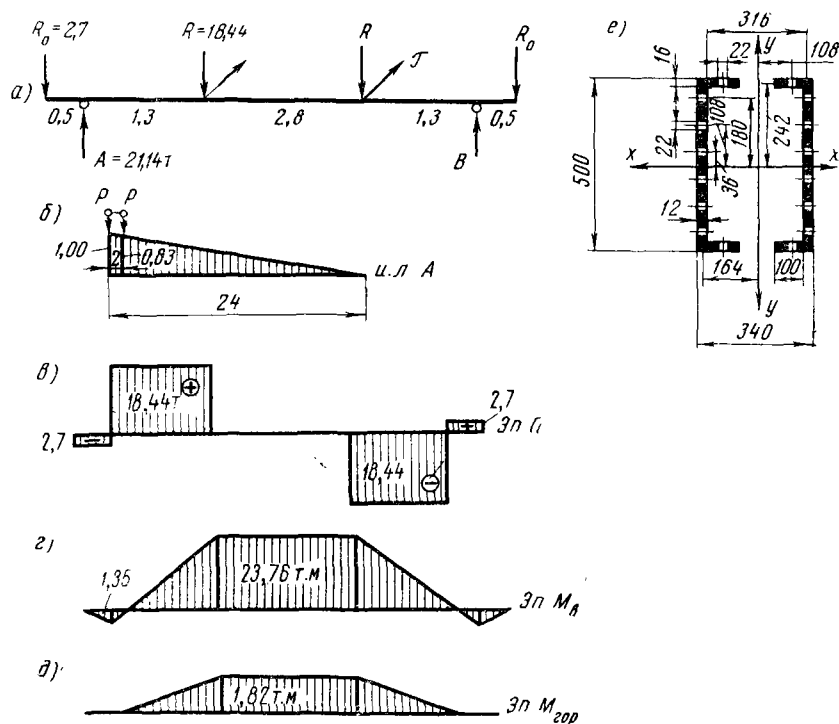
К расчету сварных опорных балок кранового моста
